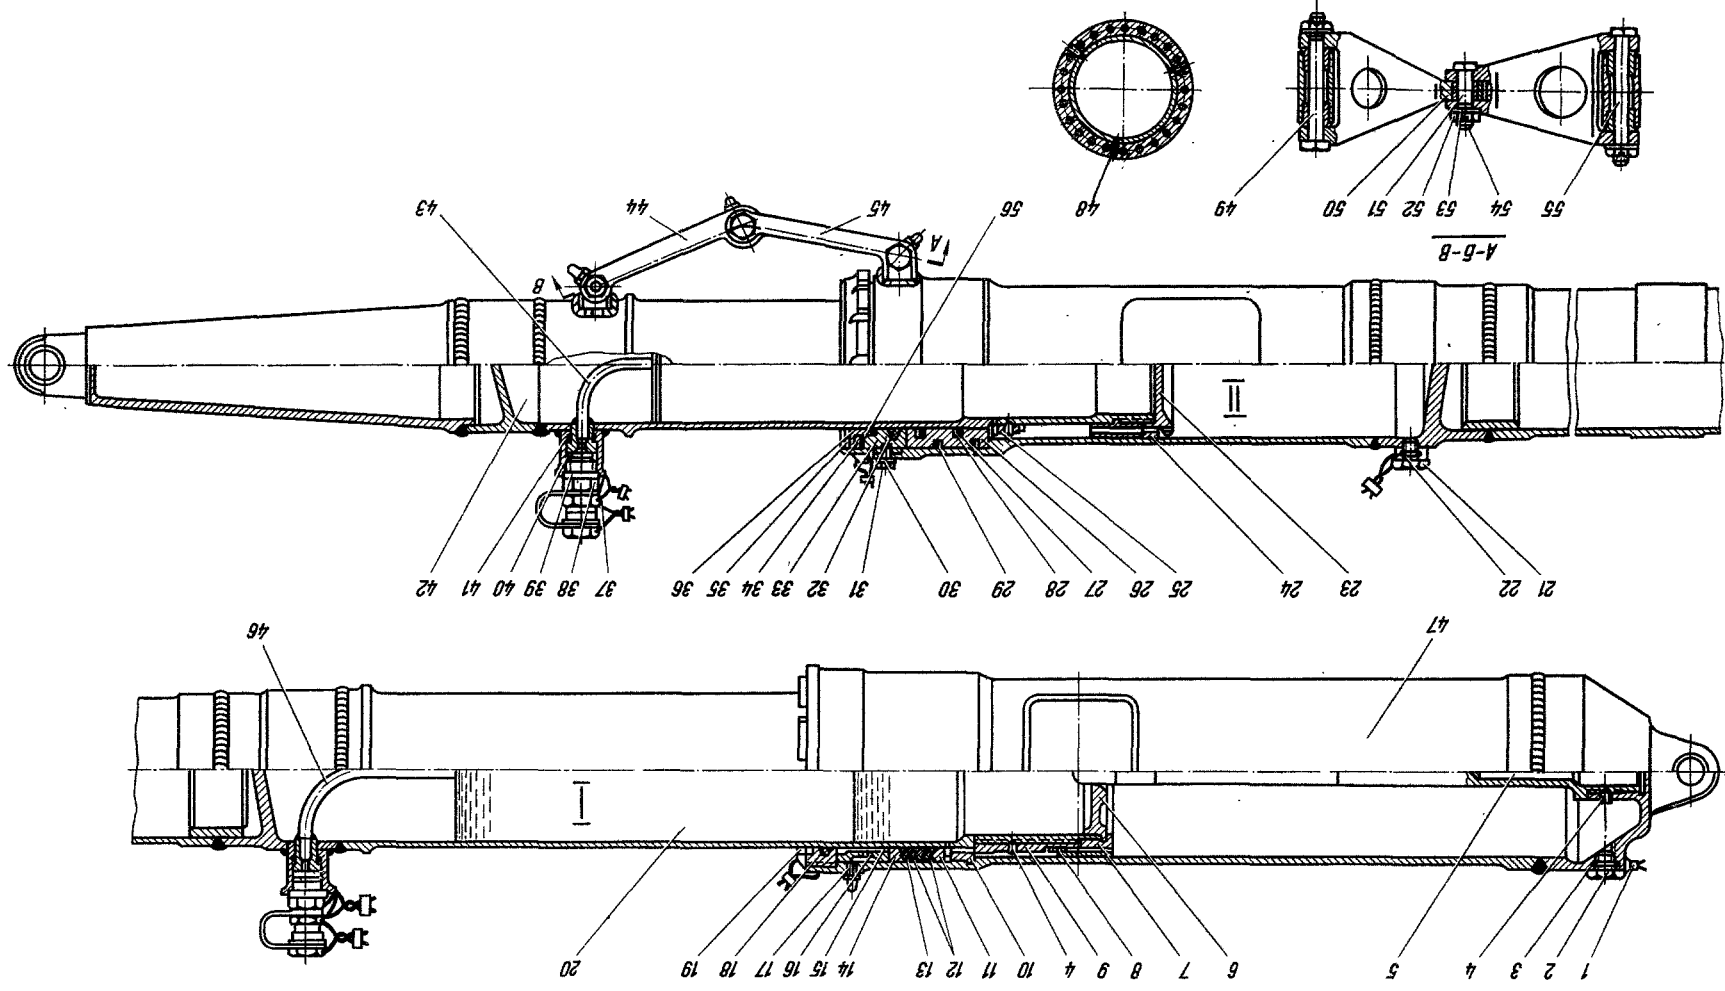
Амортизатор основного шасси 8А-4101-00-А:
